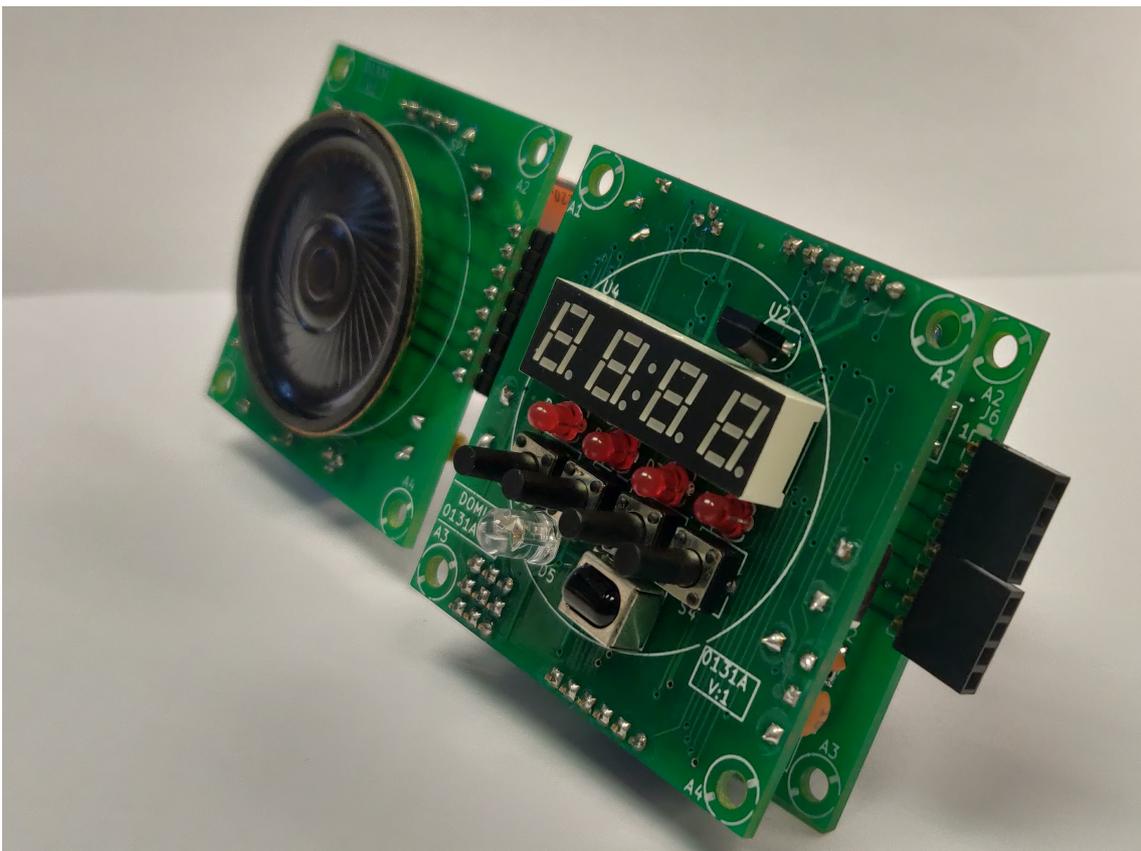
Vista lateral del montaje del sistema junto al Módulo de Control
